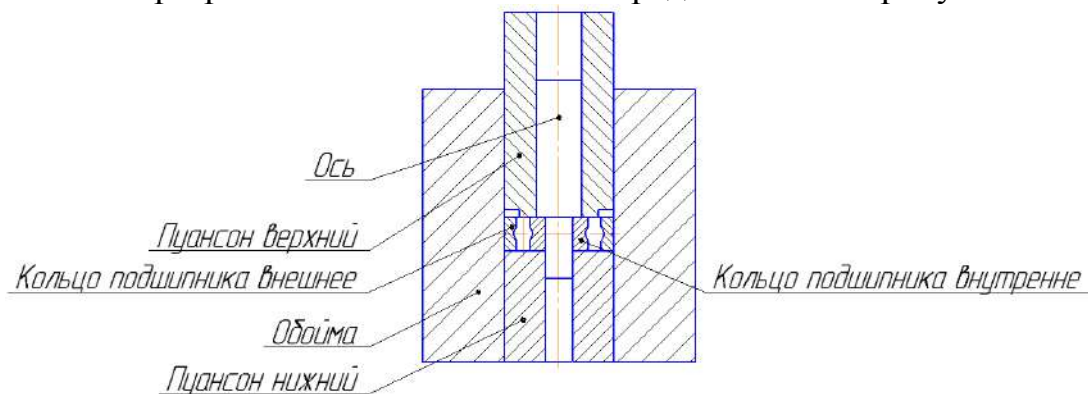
Схема оснастки для изготовления подшипника скольжения
